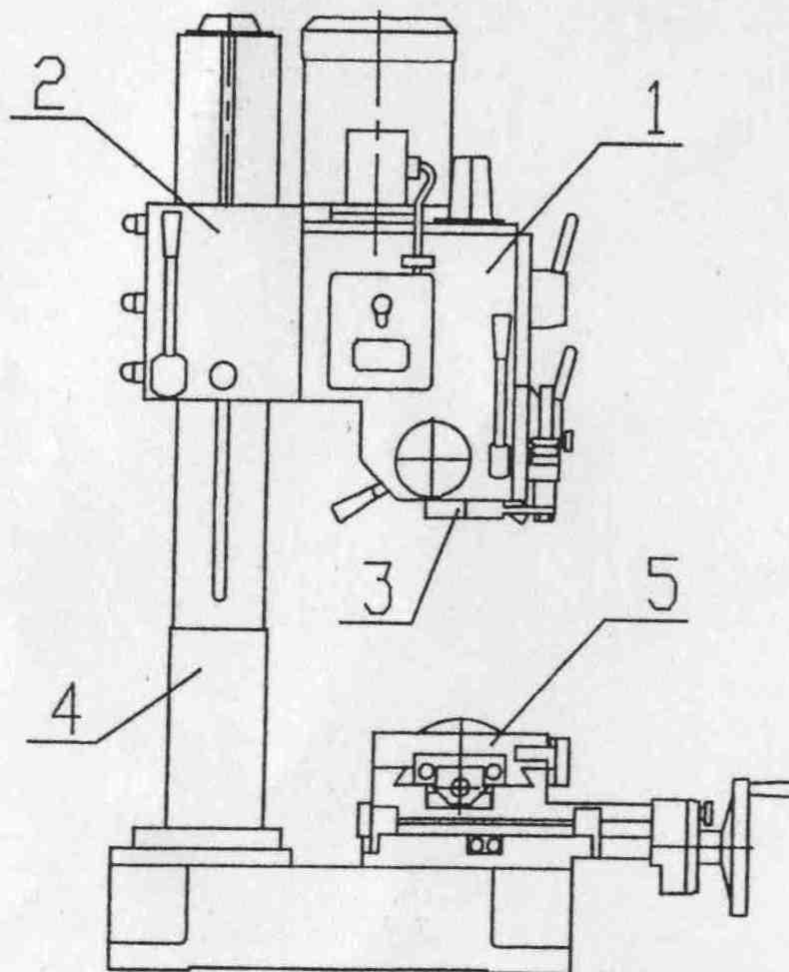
Станок настольный сверлильно-фрезерный модели ГС520
